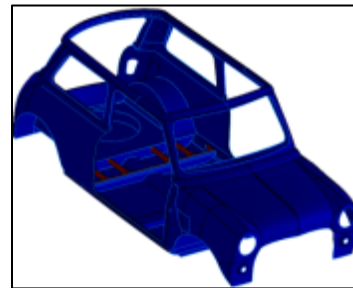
Modelado 3D de la carrocería de la MINIVAN.
